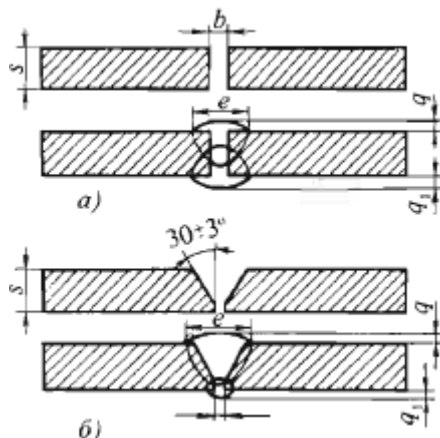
Основные конструктивные элементы сварных швов: а - без подготовки кромок малых толщин (b - ширина зазора); б - с V-образной разделкой.
